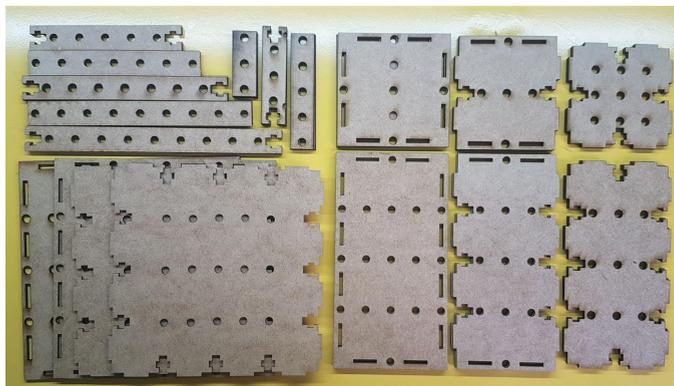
Testes para ajustes de dimensões . Fonte: A autora.
